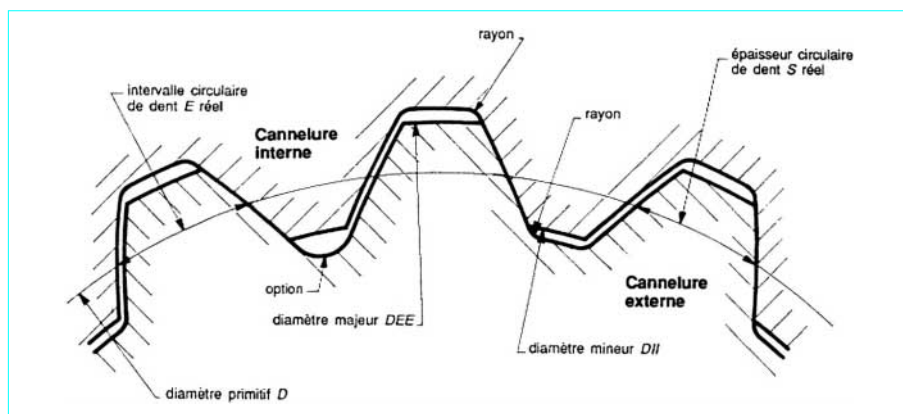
Assemblage moyeu-arbre type à considérer pour le dimensionnement
